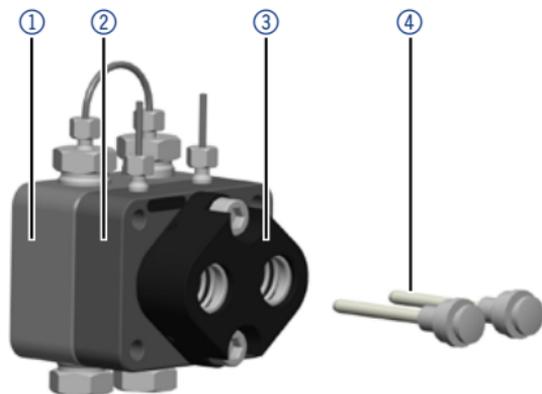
Rückansicht eines 10 ml-Pumpenkopfs
